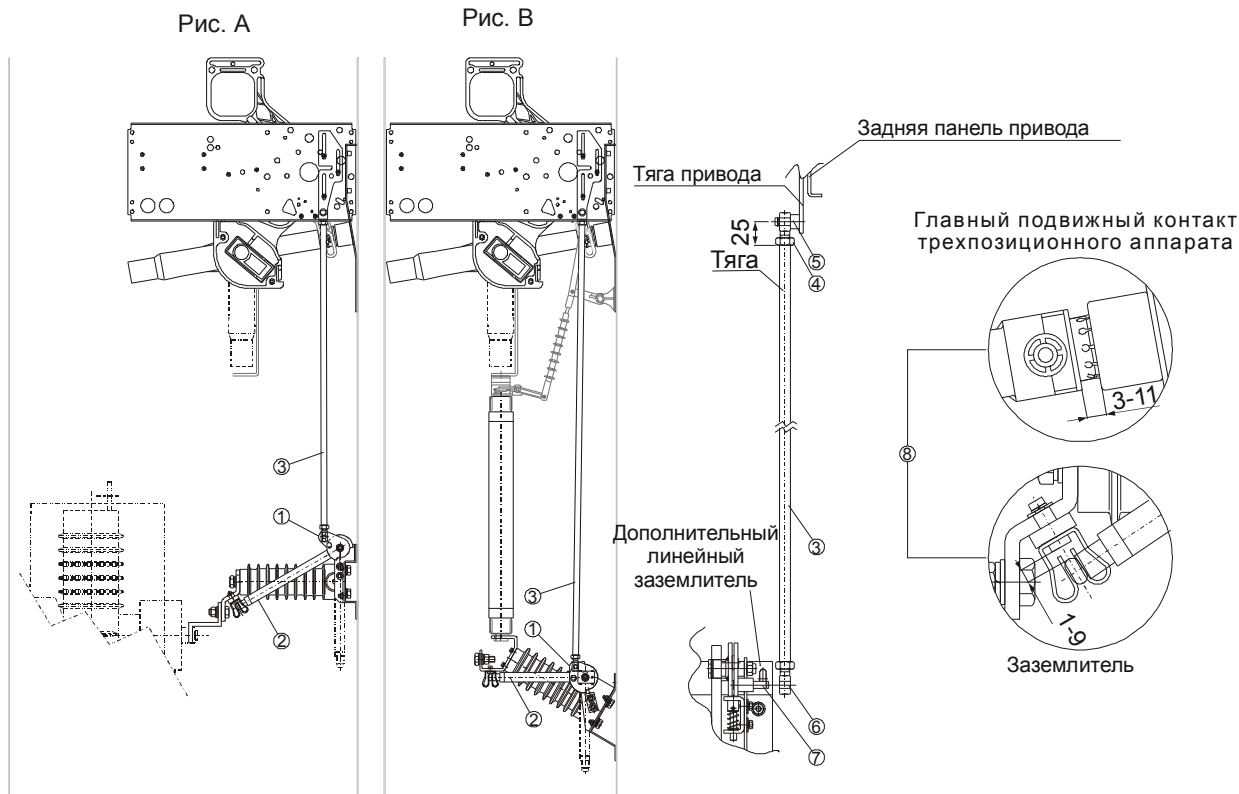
Дополнительный линейный заземляющий разъединитель. Регулировка.
